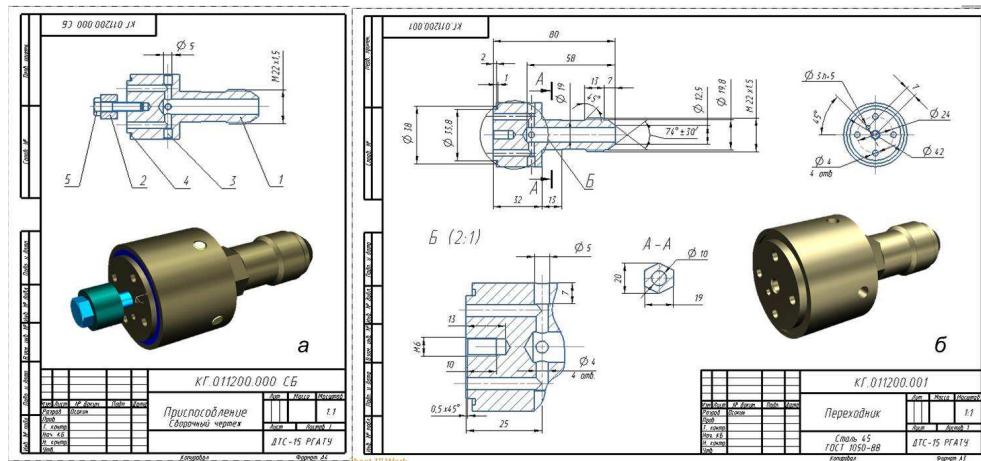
Электронная геометрическая модель сборочной единицы «приспособление» и созданный на ее основе сборочный чертеж (*a*);
